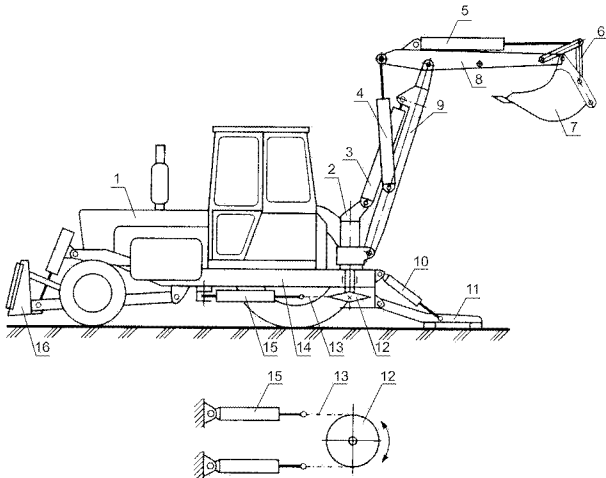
Конструктивная схема неповоротного одноковшового экскаватора:
